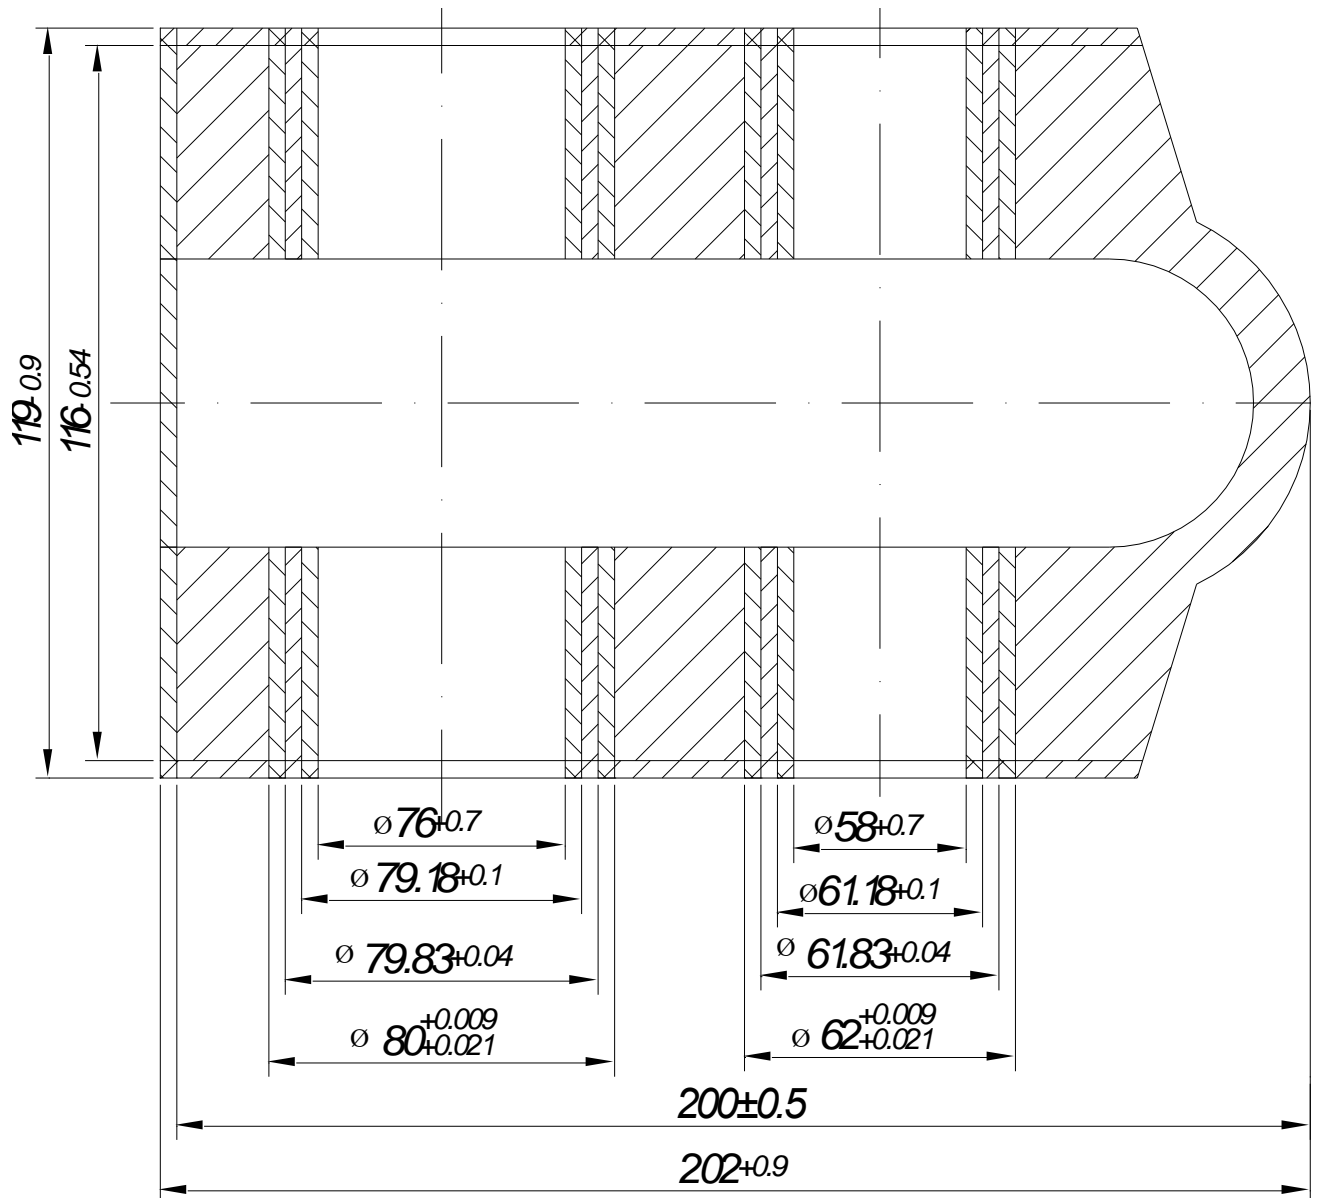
Ескіз заготовки корпуса мультиплікатора ПОЖ 16.001
